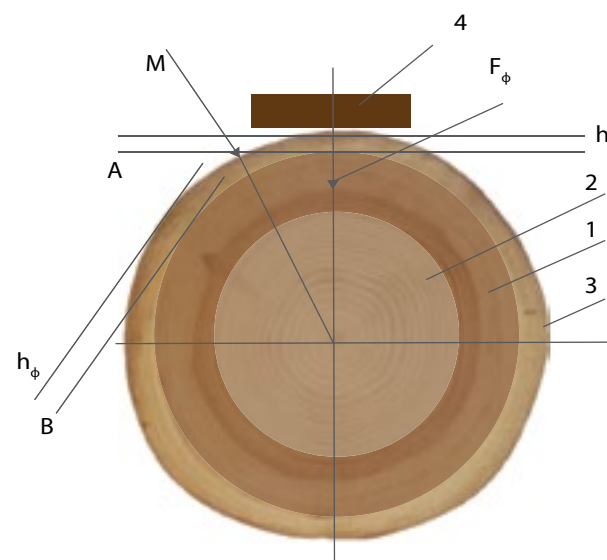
Схема для расчета глубины резания при фрезерной окорке: 1 – кора; 2 – древесина; 3 – срезаемый слой; 4 – нож фрезы
